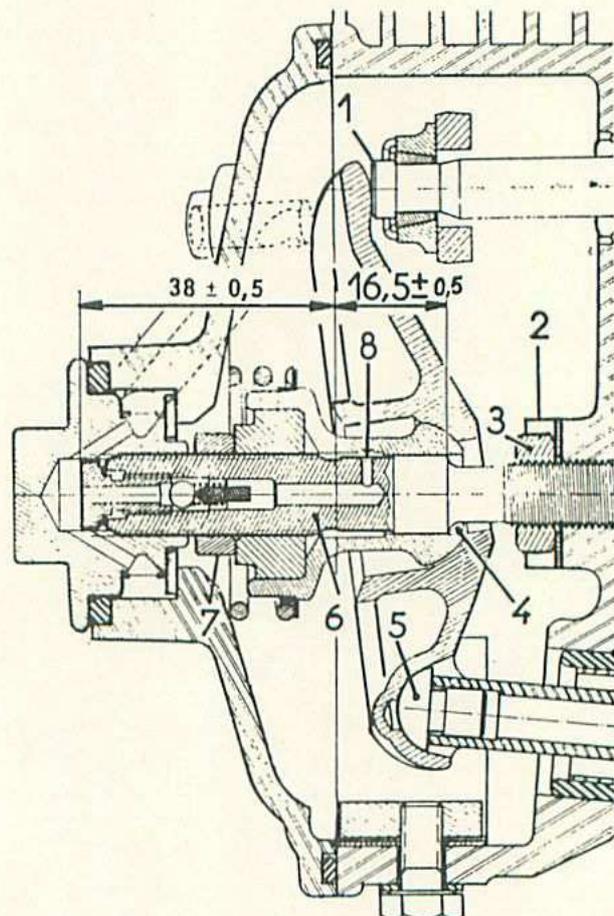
Vue en coupe d'une chambre de culbuteur.
